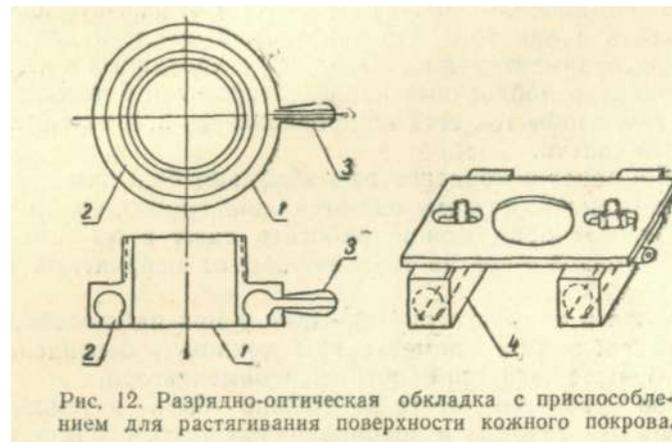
Разрядно-оптическая обкладка с приспособлением для растягивания поверхности кожного покрова.
